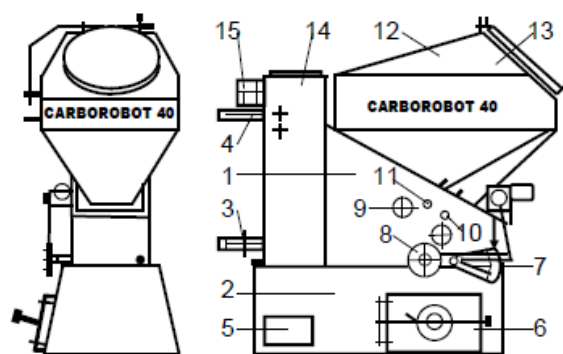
Общий вид котельного агрегата «Carborobot–40»: 1 – корпус котла;
